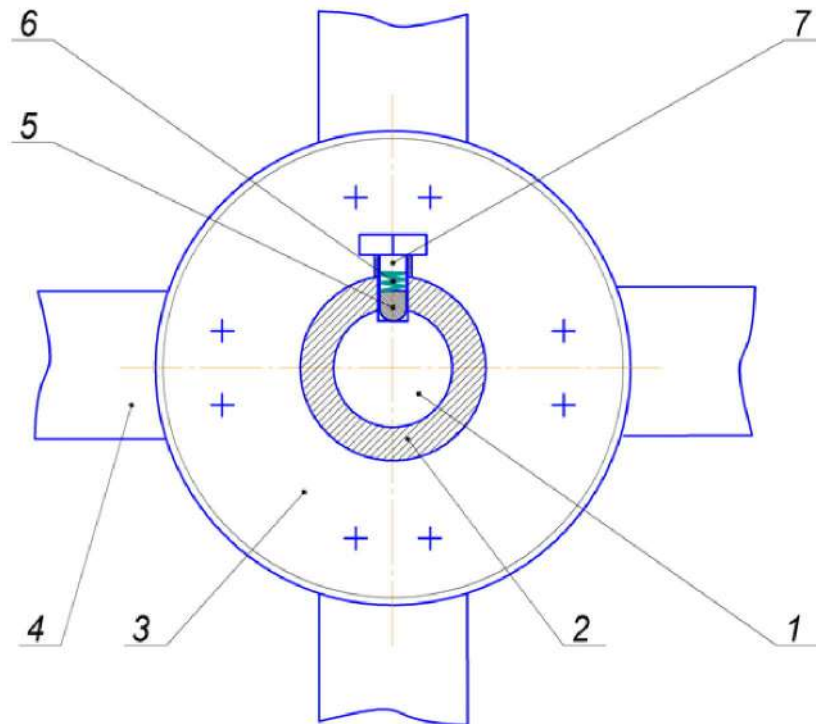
Пример предохранительного механизма фиксаторного типа для одной дисковой секции фрезы.
